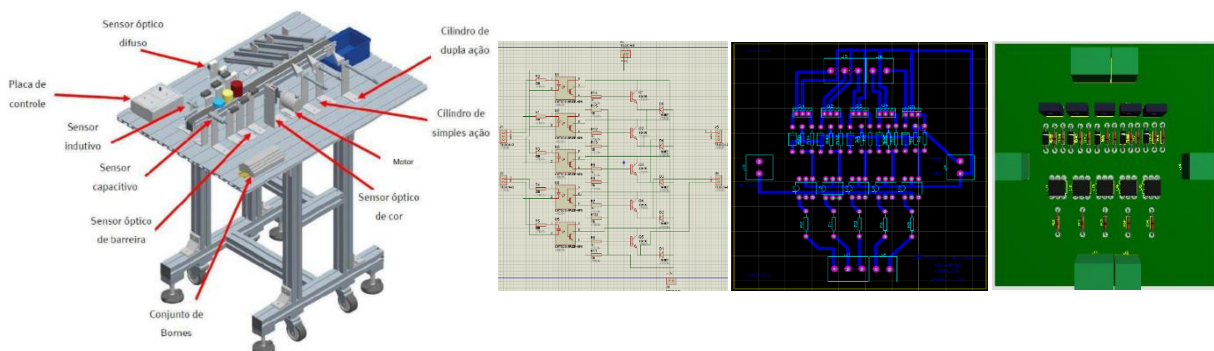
Esquemático da planta Modular Festo e placa de interface de tensão.
